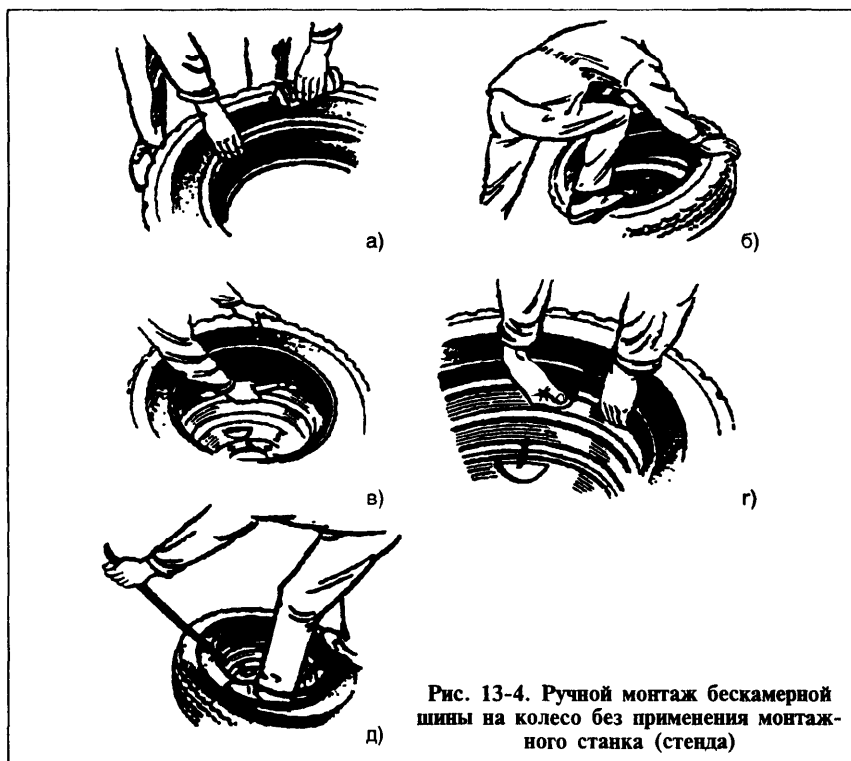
Ручной монтаж бескамерной шины на колесо без применения монтажного станка (стенда)
